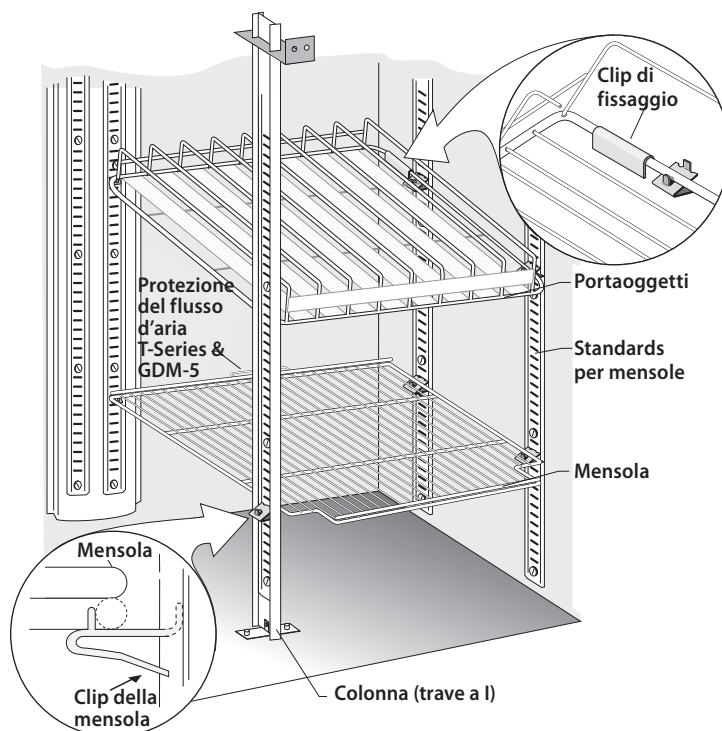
La linguetta inferiore della clip si fisserà perfettamente.
